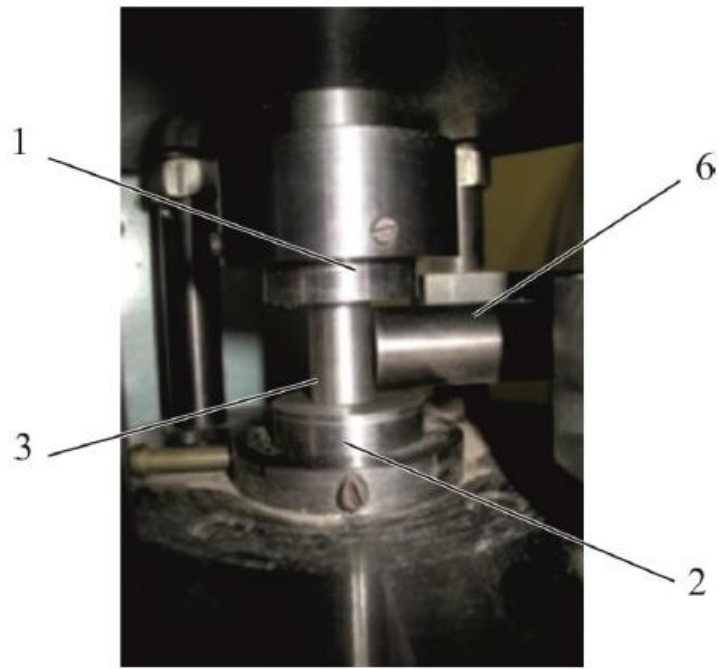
Циліндричні зразки з різними видами обробки: цифри номери партій з'єднань
